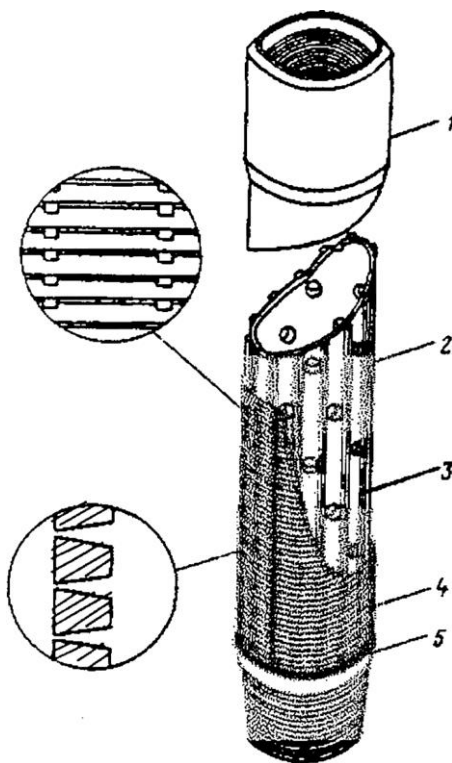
Проволочный скважинный фильтр типа ФСК: 1 – муфта; 2 – корпус; 3 – опорный стержень; 4 – профилированная проволока; 5 – сварной шов.
